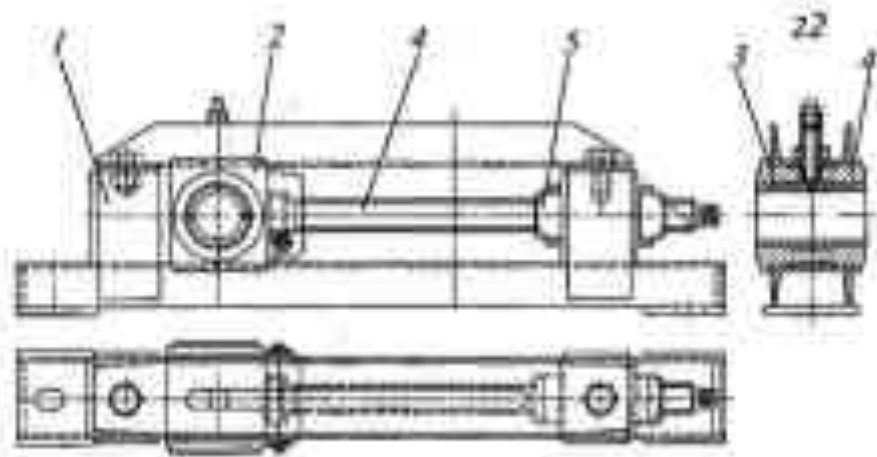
Гвинтовий натяжний пристрій: 1 – корпус; 2 – повзун; 3 – вкладиш; 4 – гвинт; 5 – гайка
